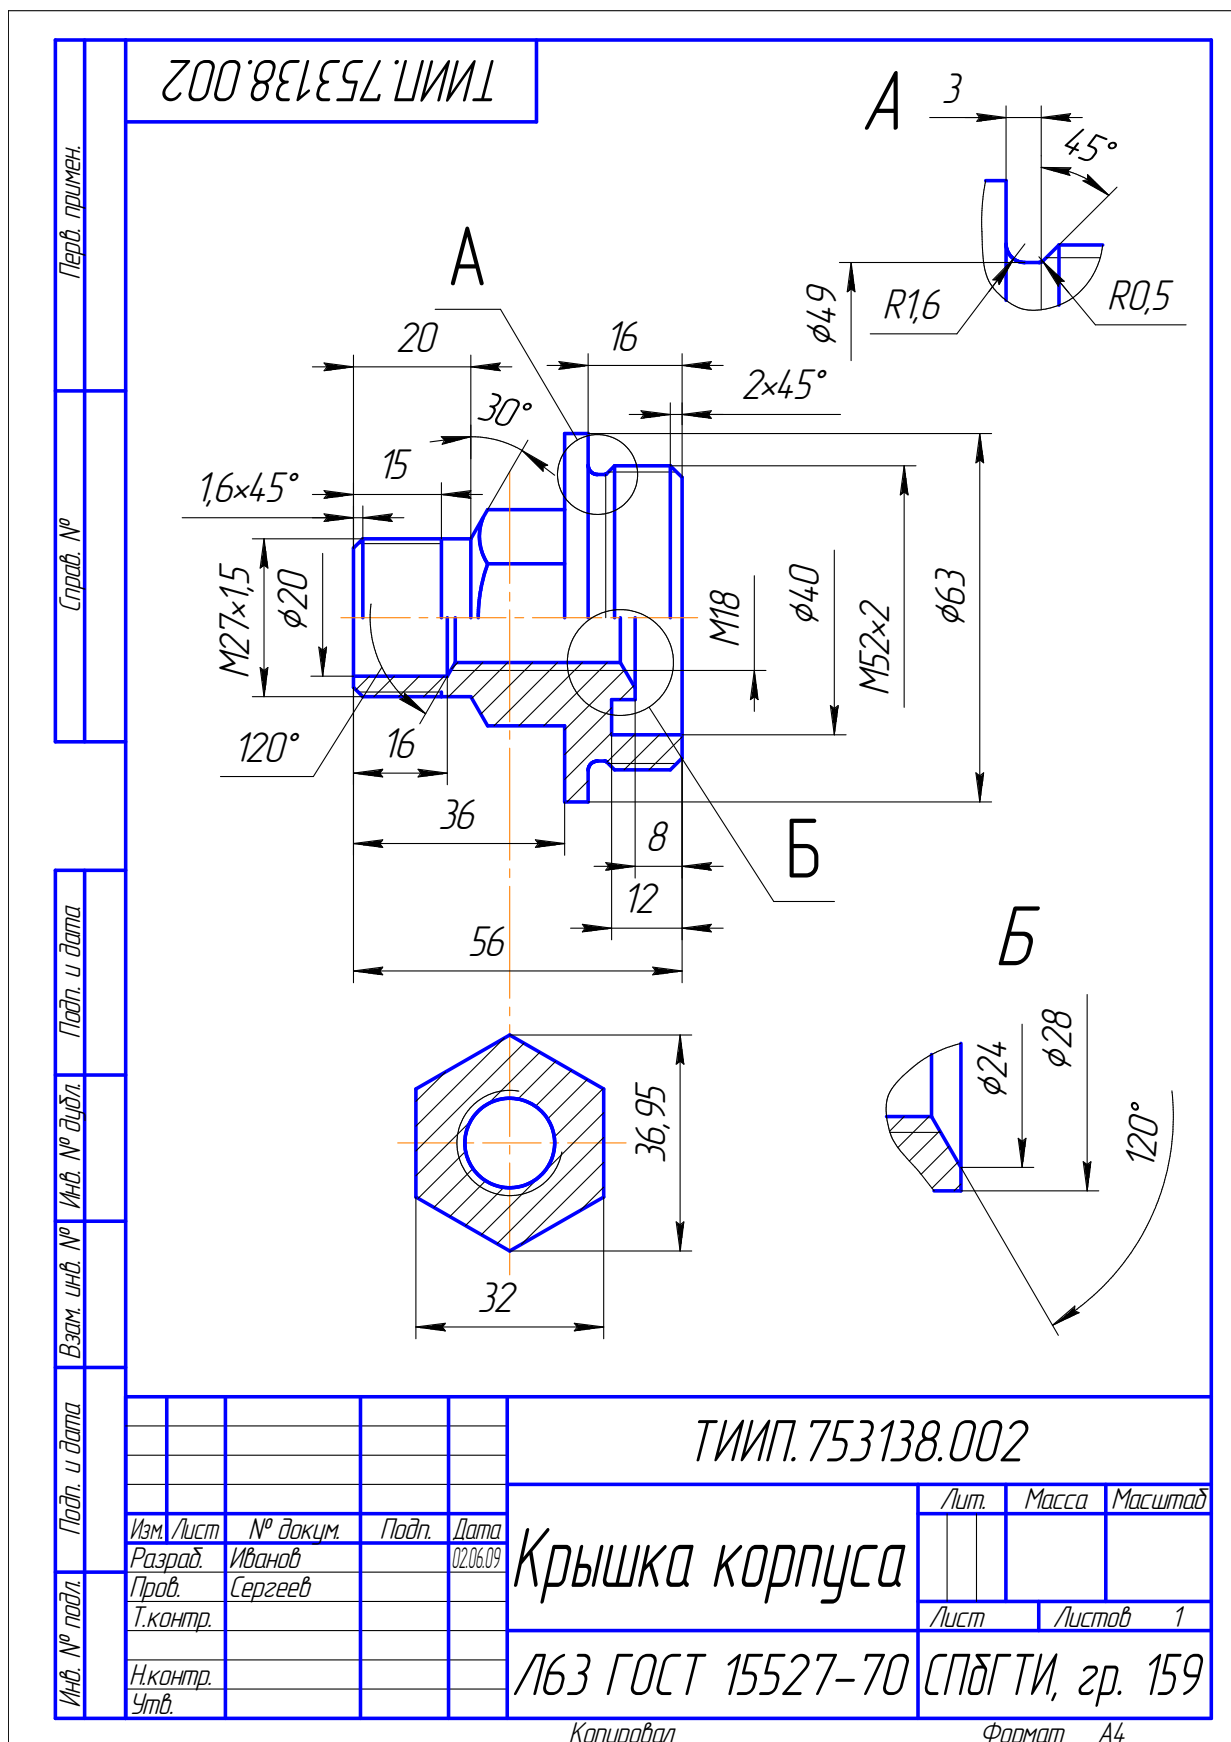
Пример выполнения эскиза (рабочего чертежа). Типовой элемент «Крышка корпуса»
